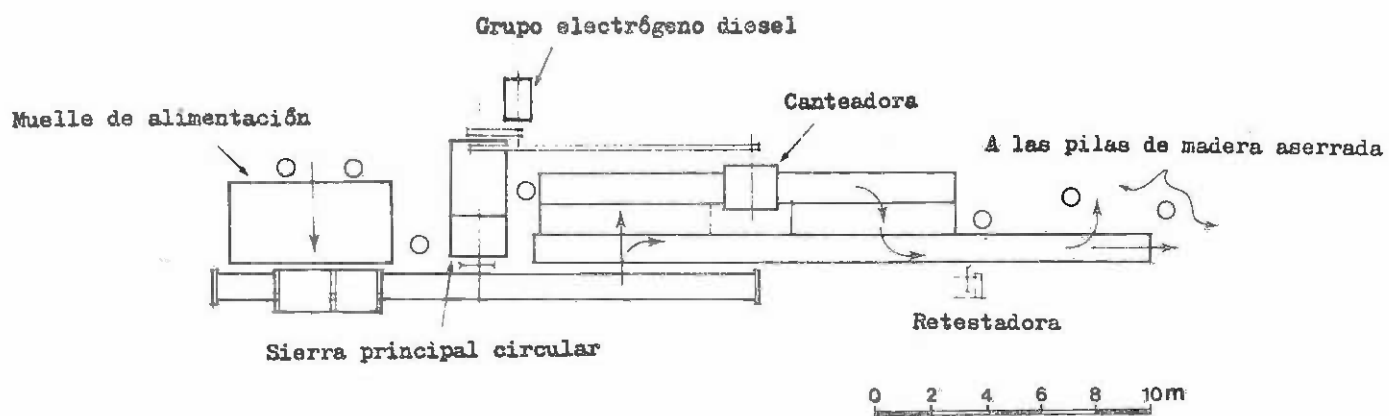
DISEÑO DE UN ASERRADERO PEQUEÑO, MOVIL O PORTATIL
